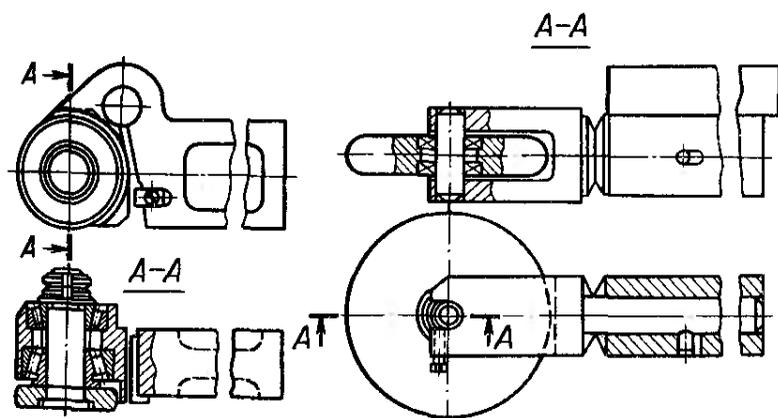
Інструмент для обкатування зовнішніх циліндричних поверхонь.
